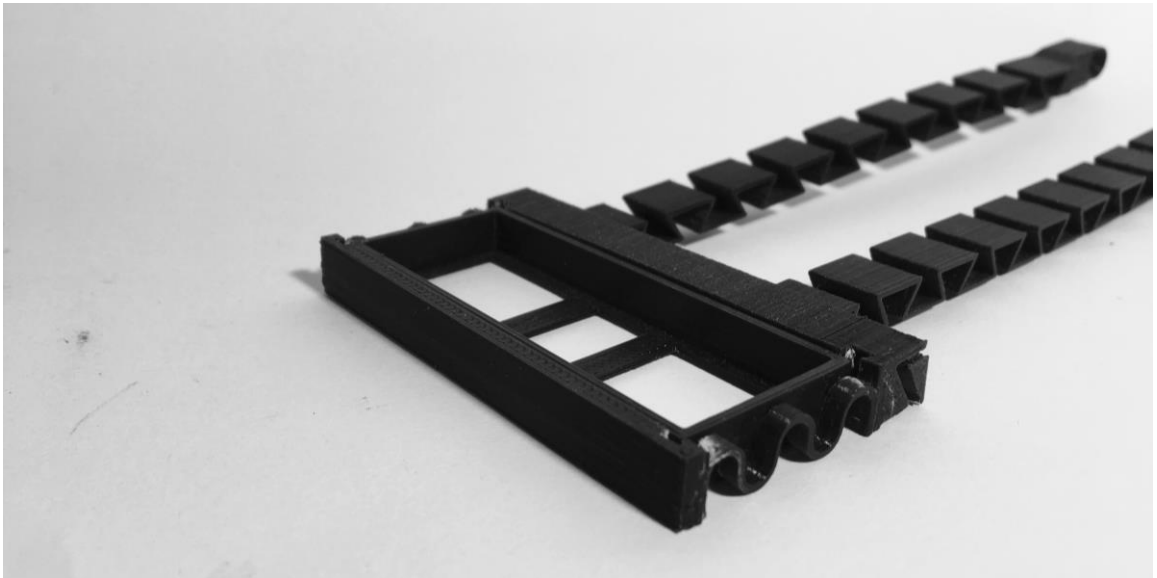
Primeiro protótipo do módulo principal com sistema de extração.
